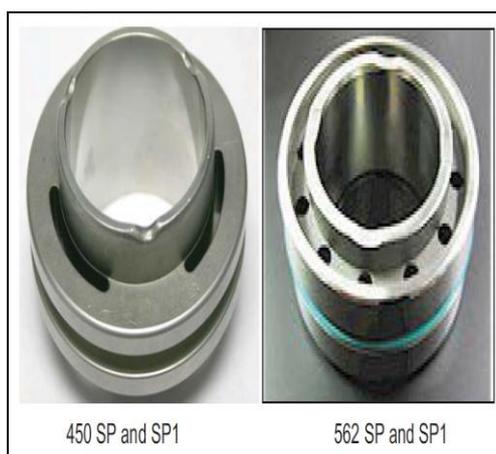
Pre- ensamble de t-ring en el motor bearing.
